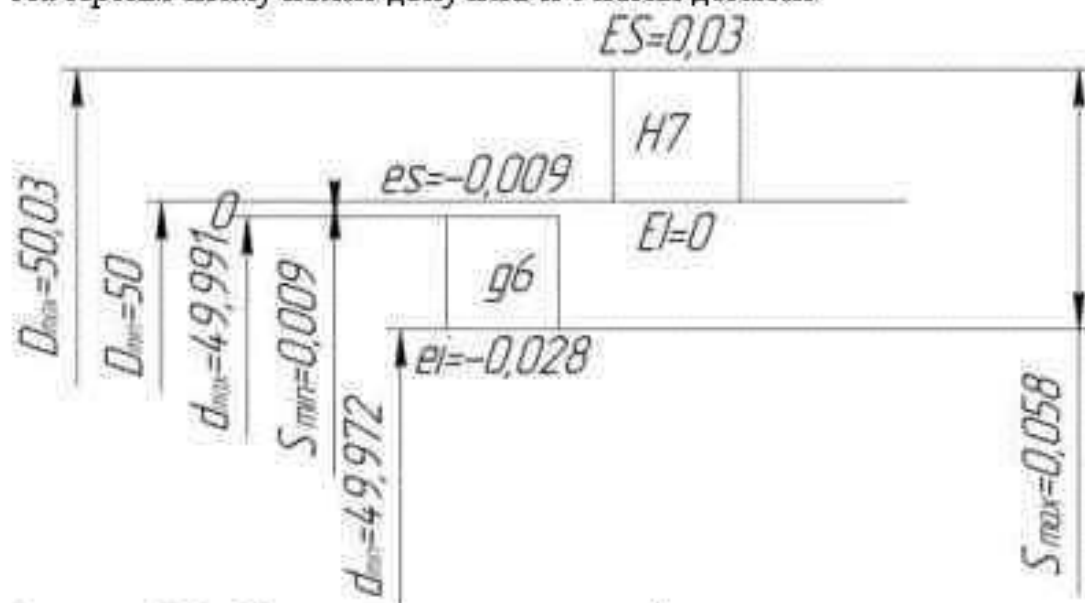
Схема расположения полей допусков отверстия и вала
